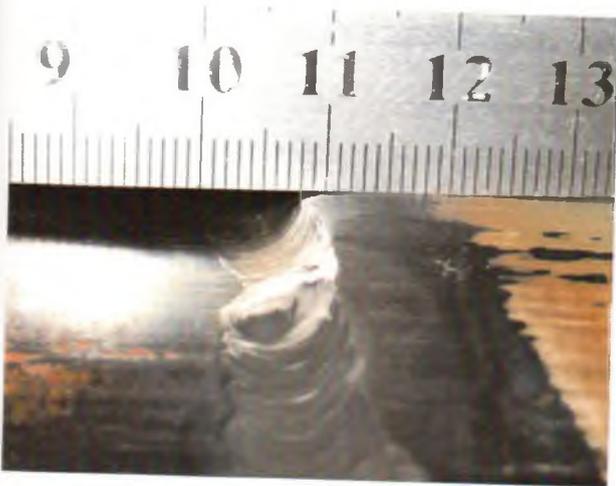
Смещение кромок в стыковом сварном соединении трубопровода. Продольные оси свариваемых деталей испытывают только линейное смещение, угловое смещение отсутствует
